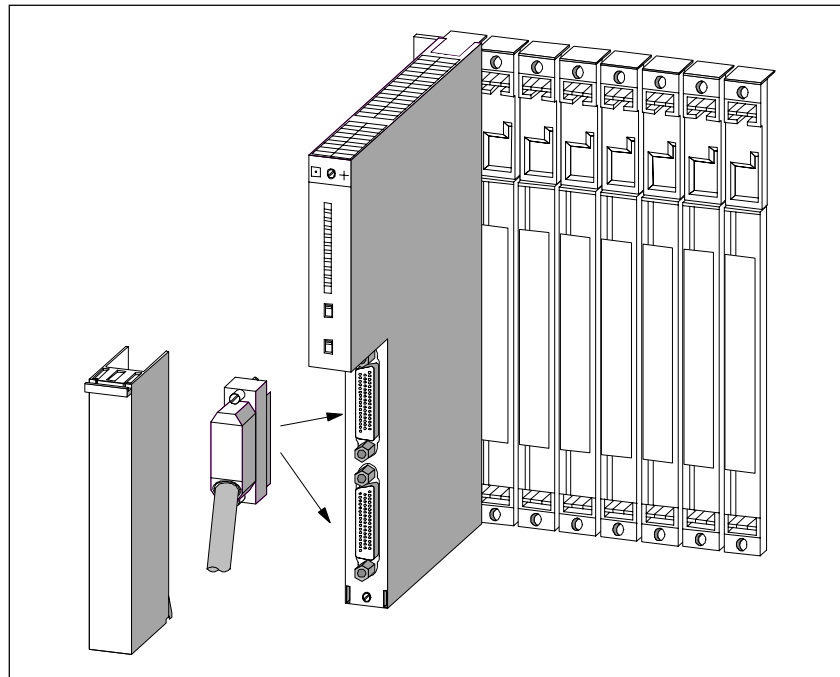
Вставка соединительного кабеля в передающий ИМ
